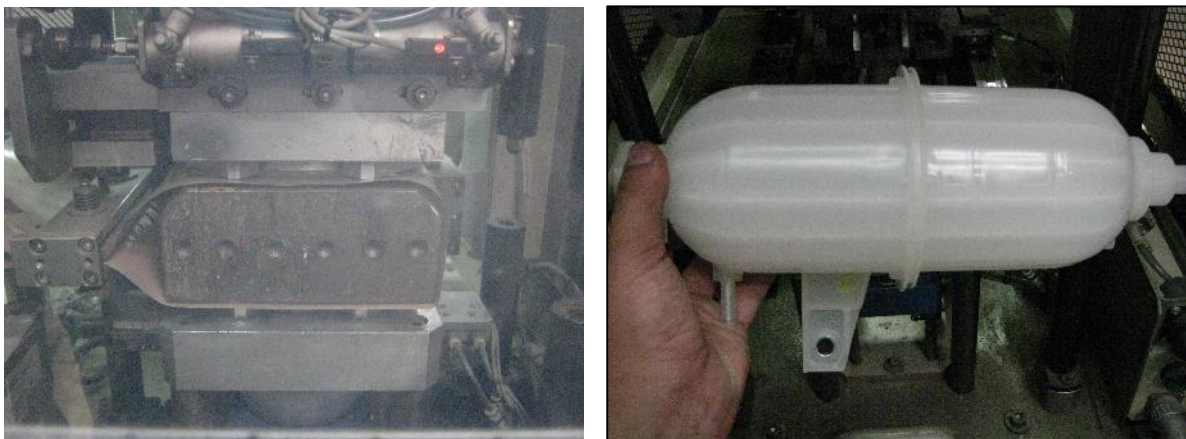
Operación de calentamiento y resultado luego de la soldadura
